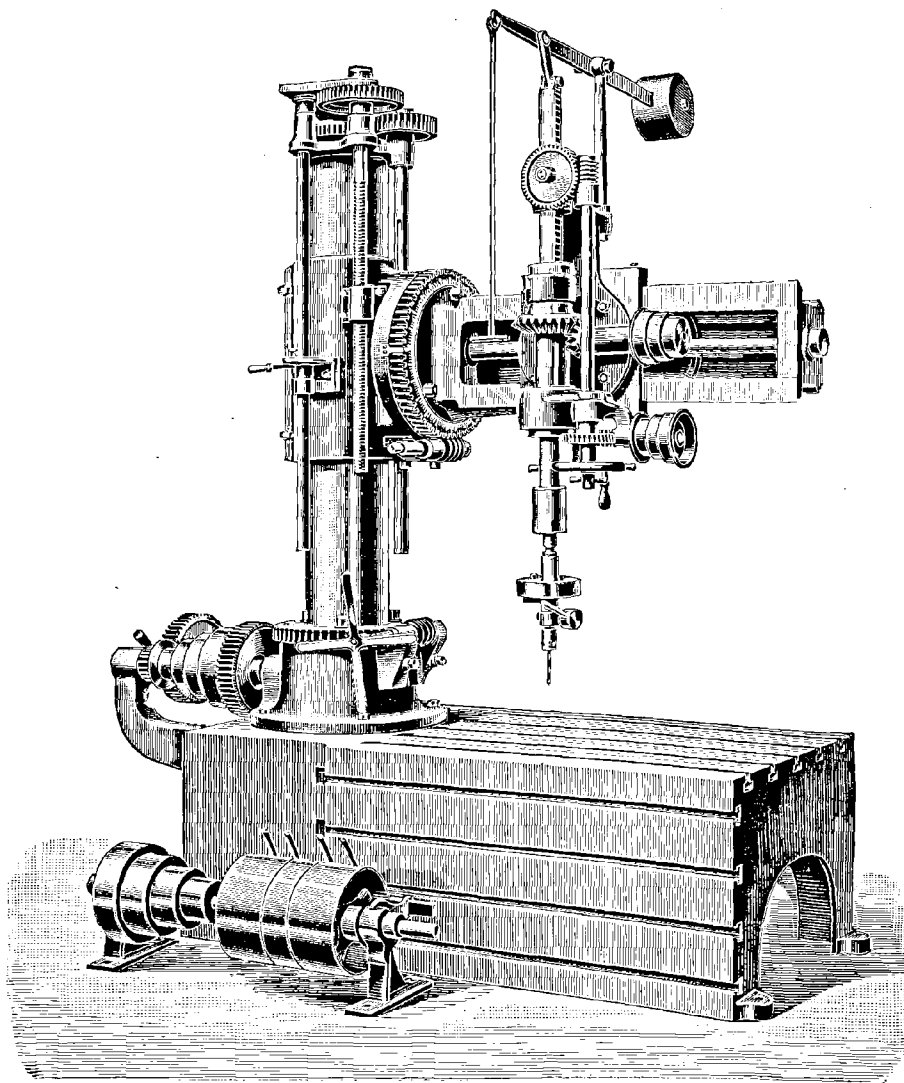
Machine à percer radiale Queen de M. Besse.
